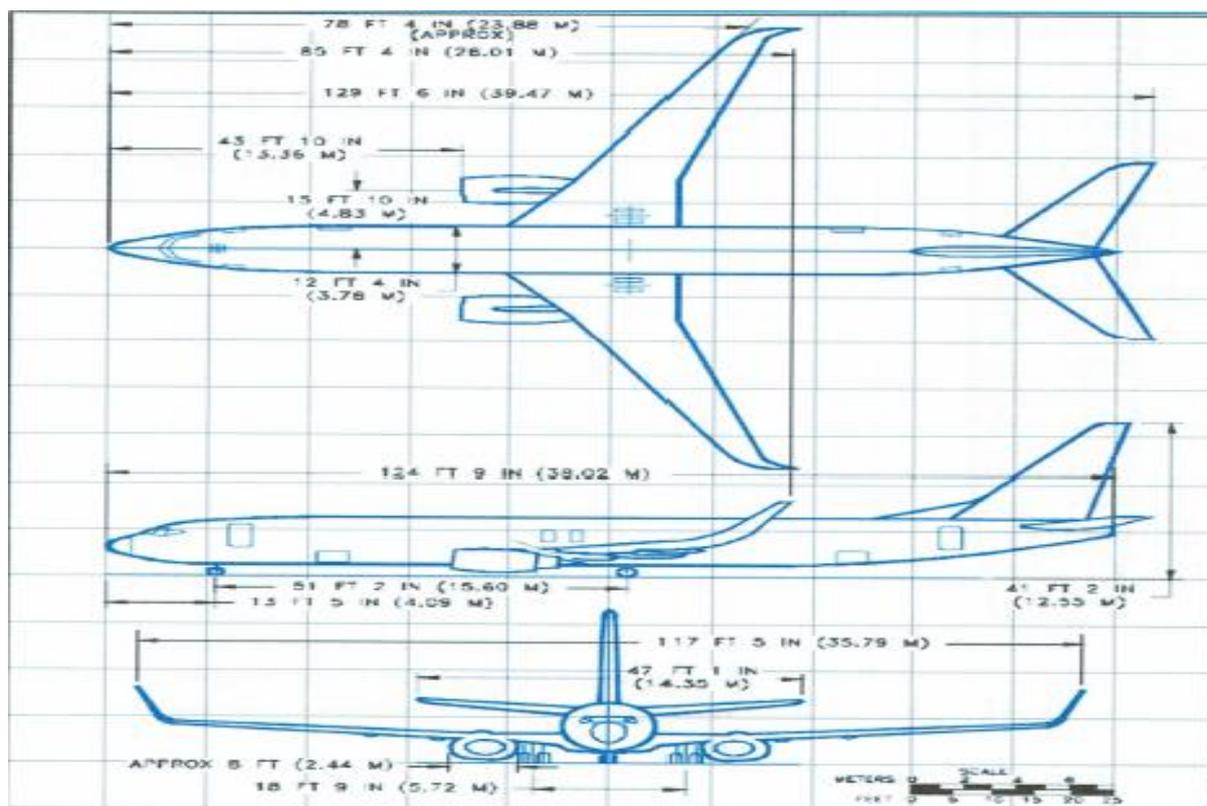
Arrangement générale et les premières dimensions pour une configuration avec Winglets B737-800
